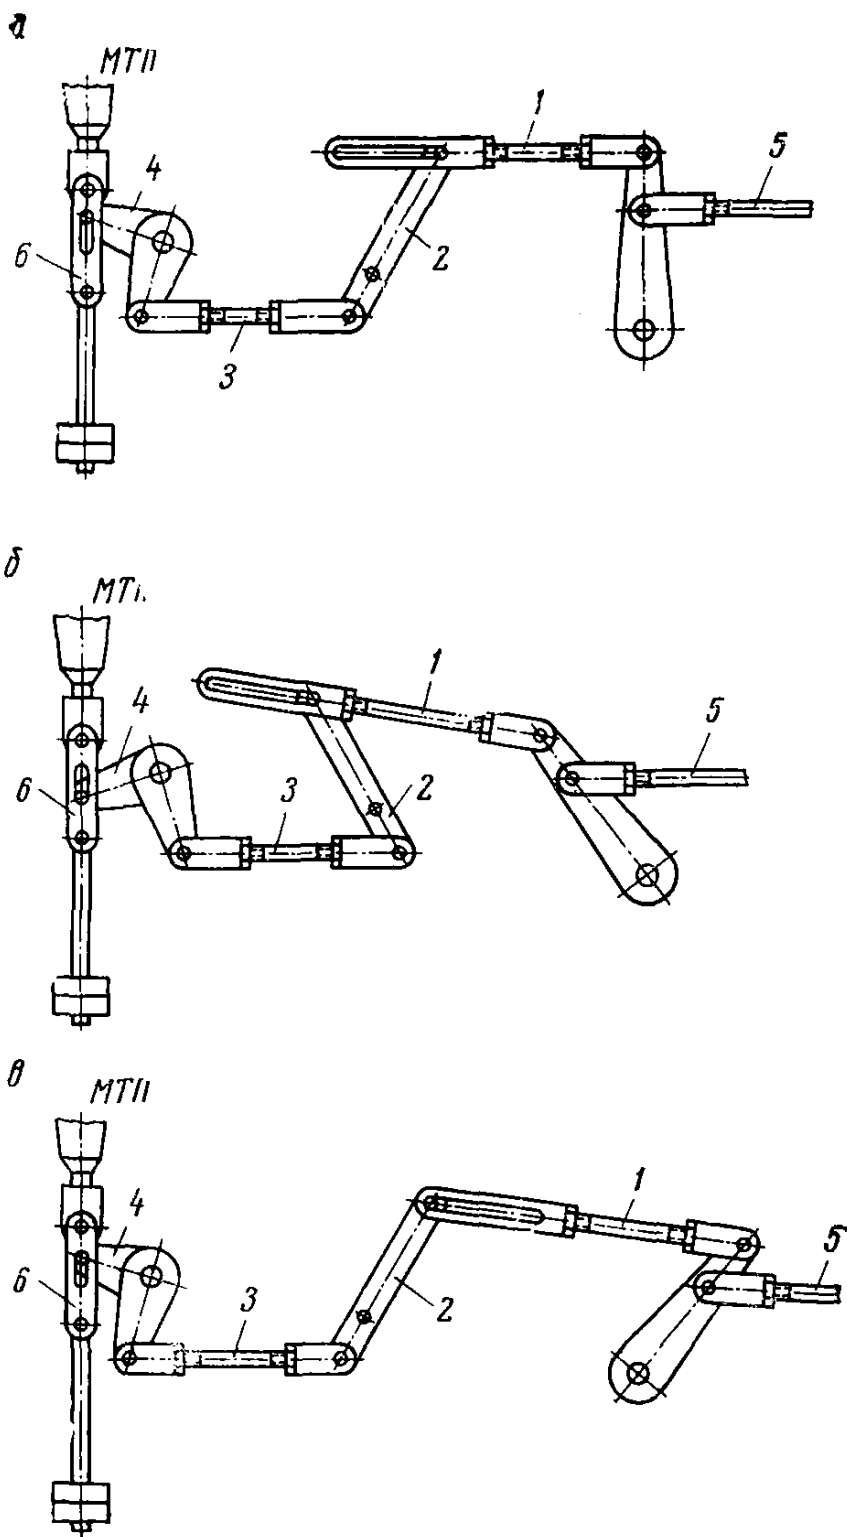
Схема устройств включения предохранительного торможения от рукоятки РПТ:
